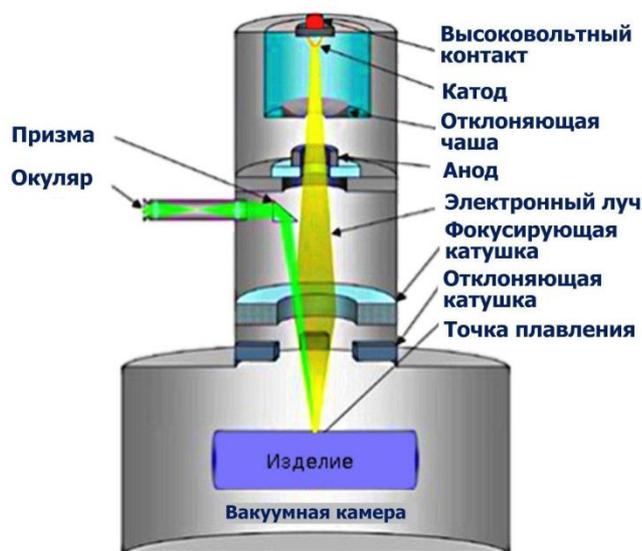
Схема электронно-лучевой сварки
